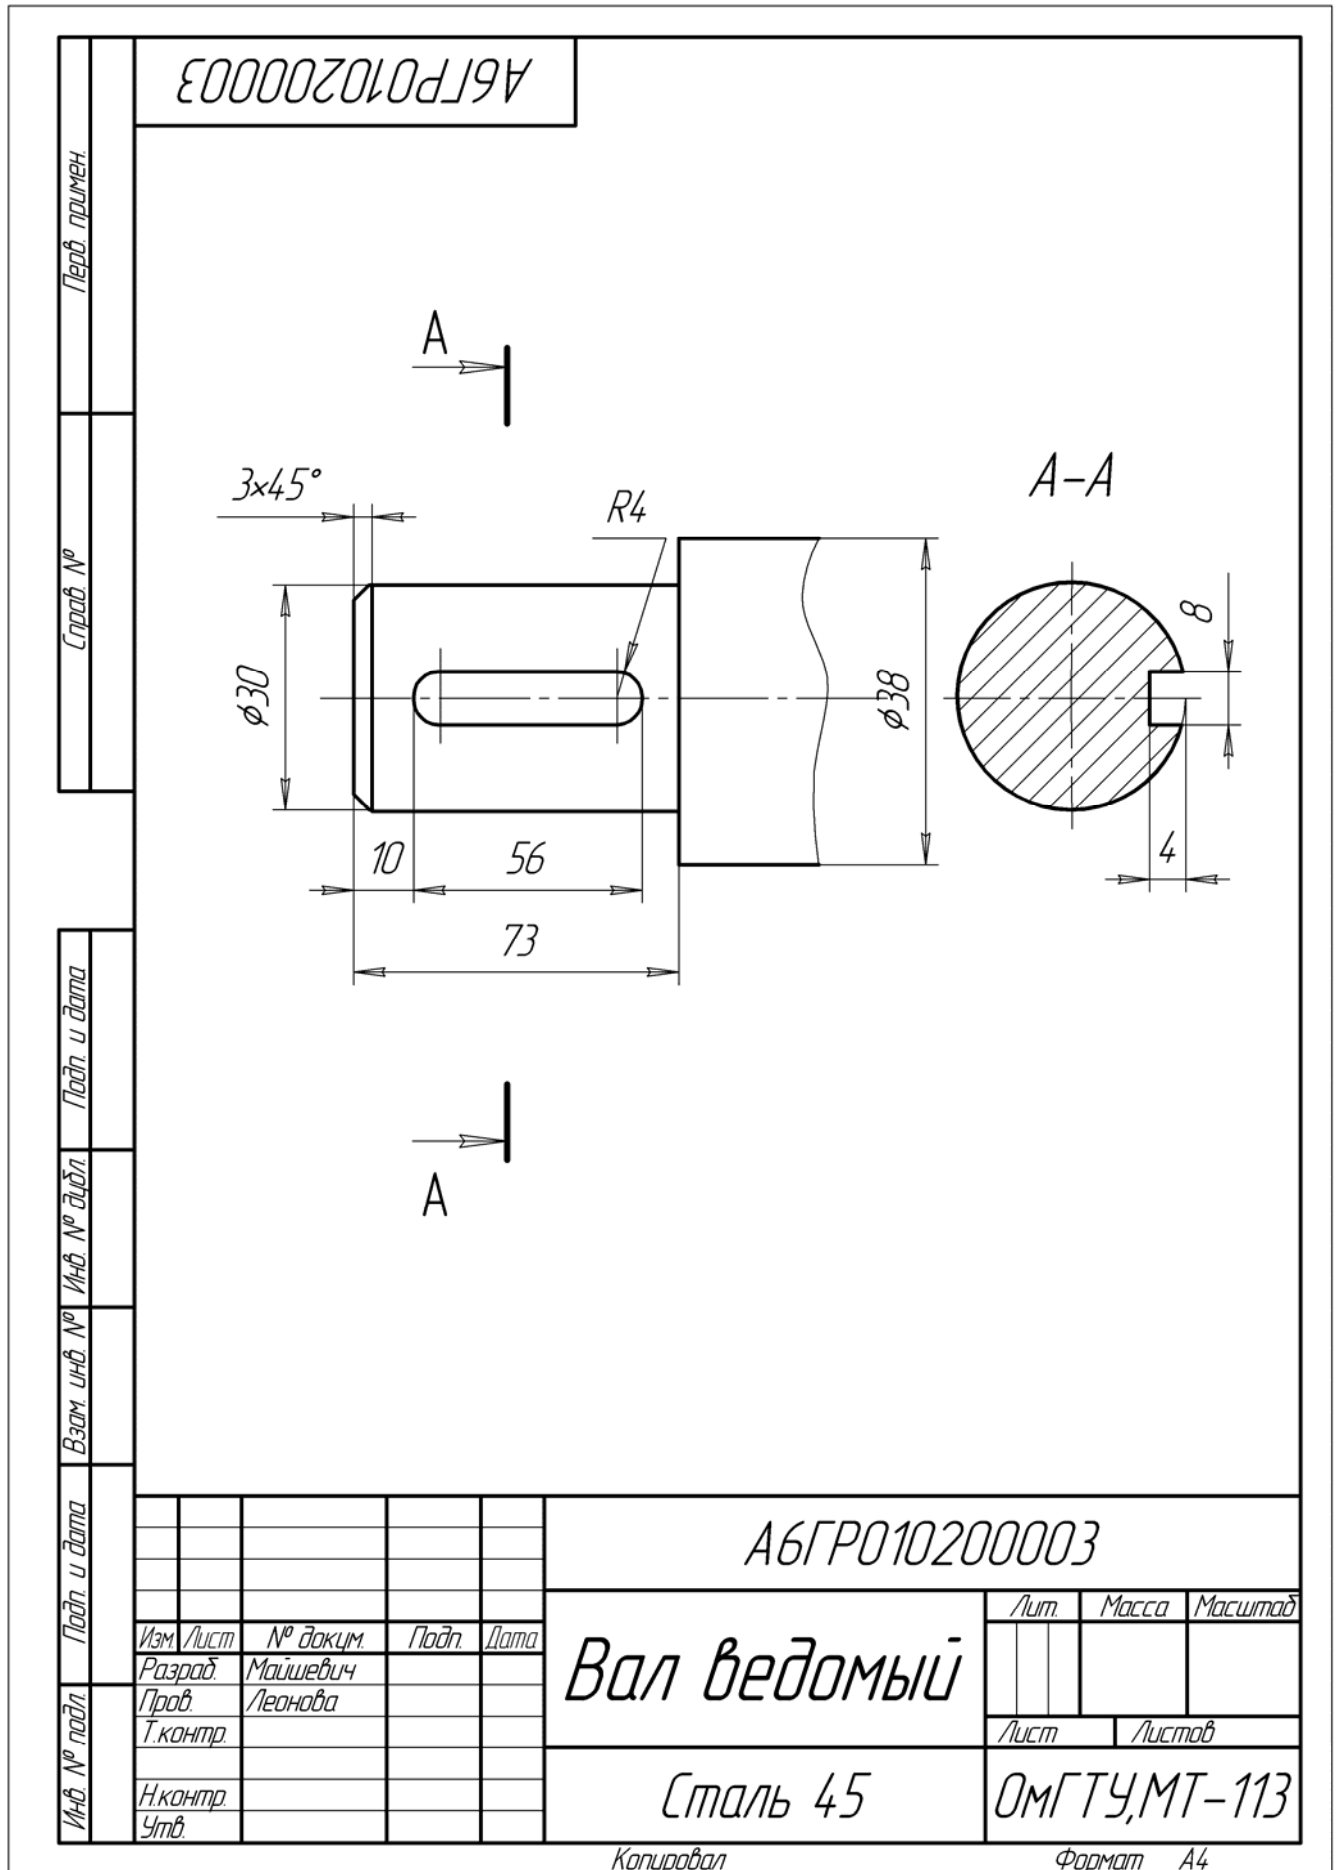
Рабочий чертеж хвостовика ведомого вала
